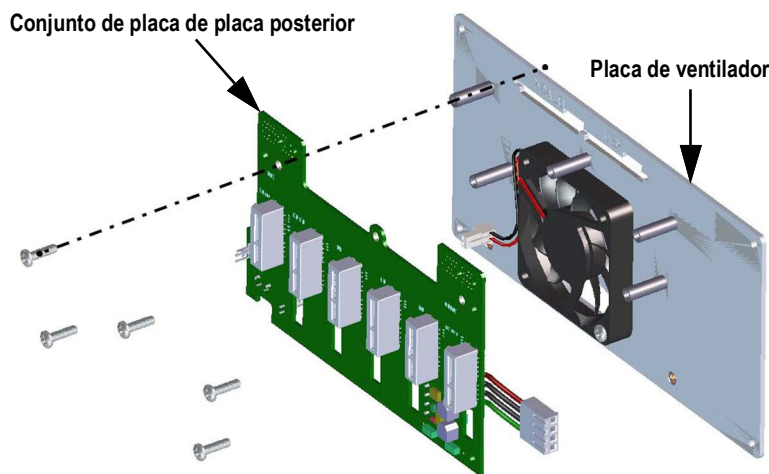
Desmontaje del conjunto de placa de placa posterior
